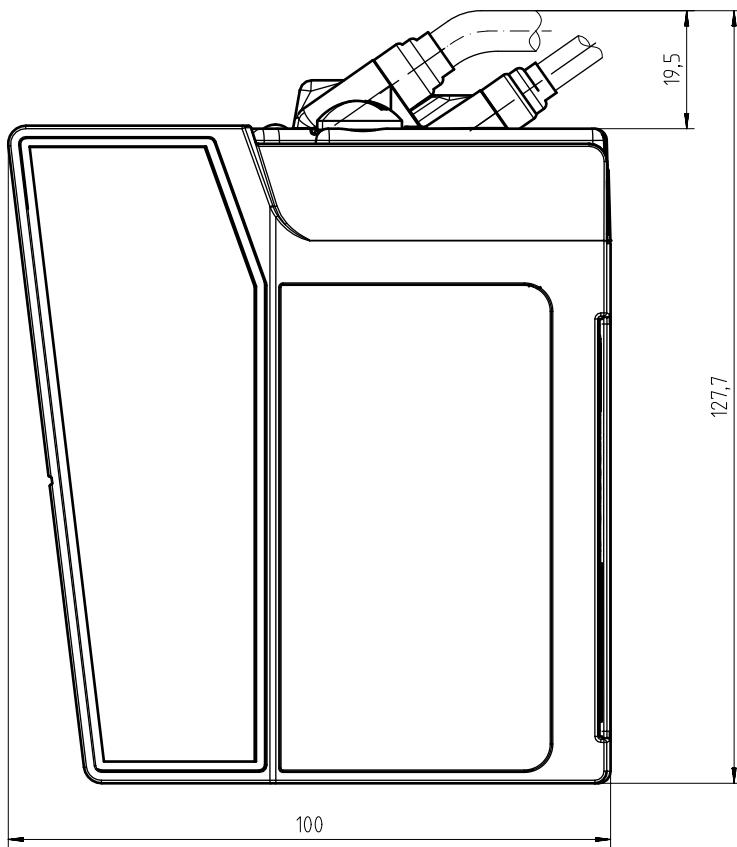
Maßzeichnung BPS mit Anschlusshaube ME 348
